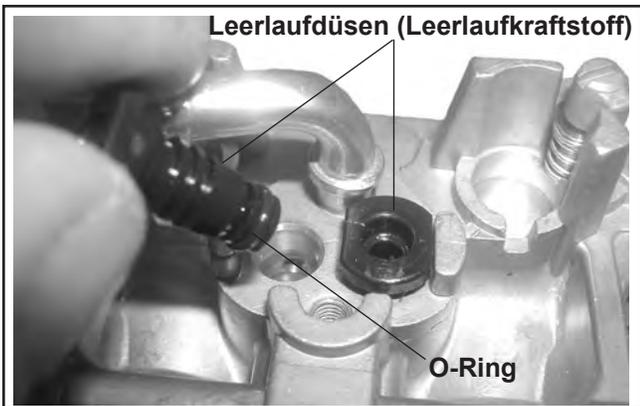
Detailansicht O-Ring und Leerlaufdüsen.
